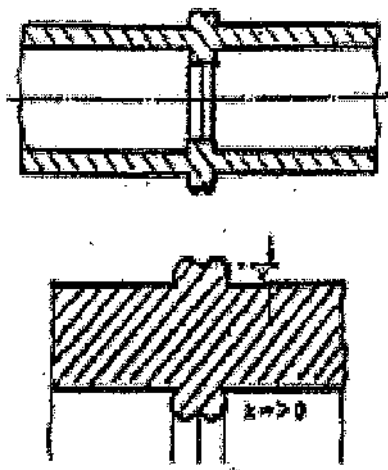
Схема стыковой сварки труб при помощи нагревательного элемента
